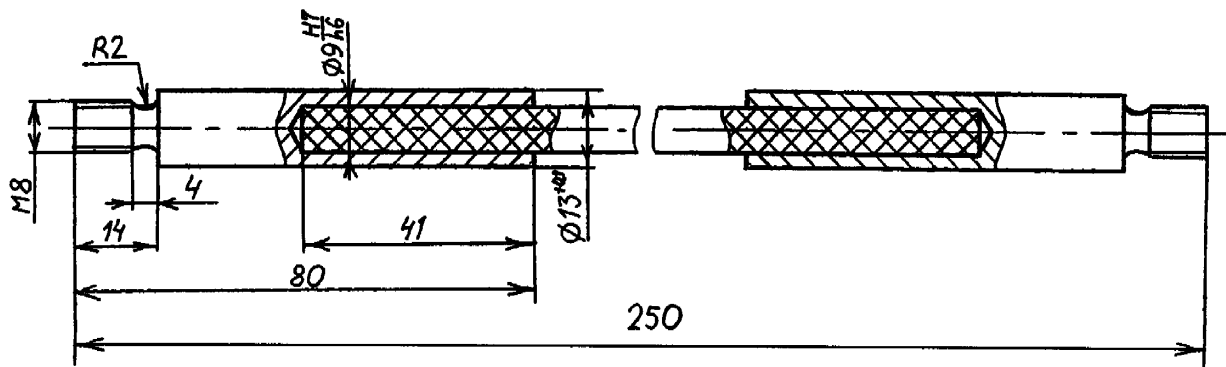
Ескіз зразка для випробування з'єднання головки насосної штанги зі склопластиковим тілом на статичний розтяг
